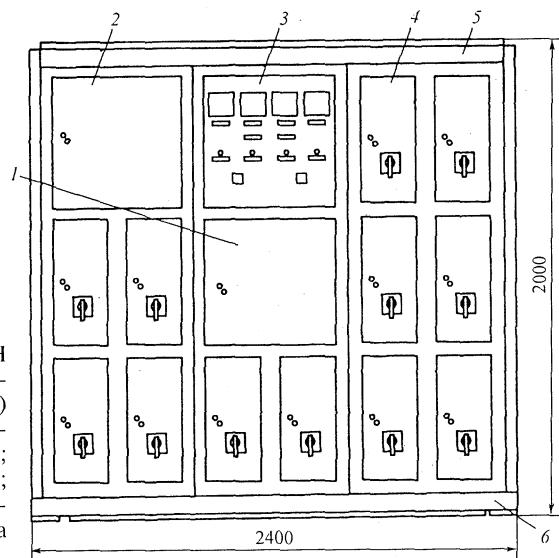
Вариант конструкции РУНН с выдвижными выключателями (габаритные размеры, мм: 2400 × 2000 × 825) (исполнение с АВР — неявный ввод резерва): 1 — шкаф выключателя ввода; 2 — шкаф секционного выключателя; 3 — шкаф релейный; 4 — шкаф линейного выключателя; 5 — рама; 6 — рама основания
